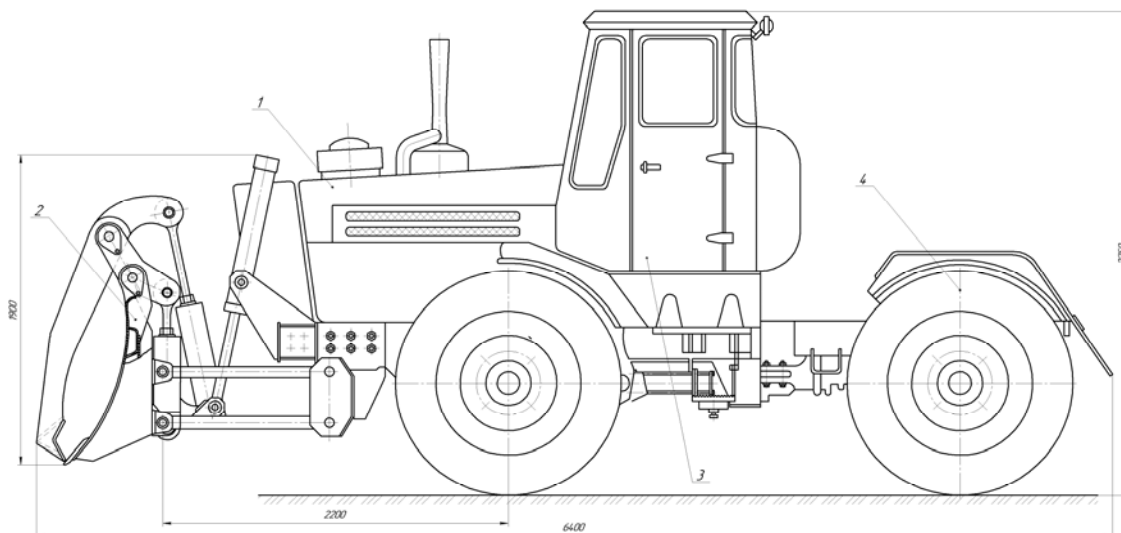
Загальний вид робочого устаткування з захватним пристроєм на базі шарнірно-зчленованого колісного шасі
